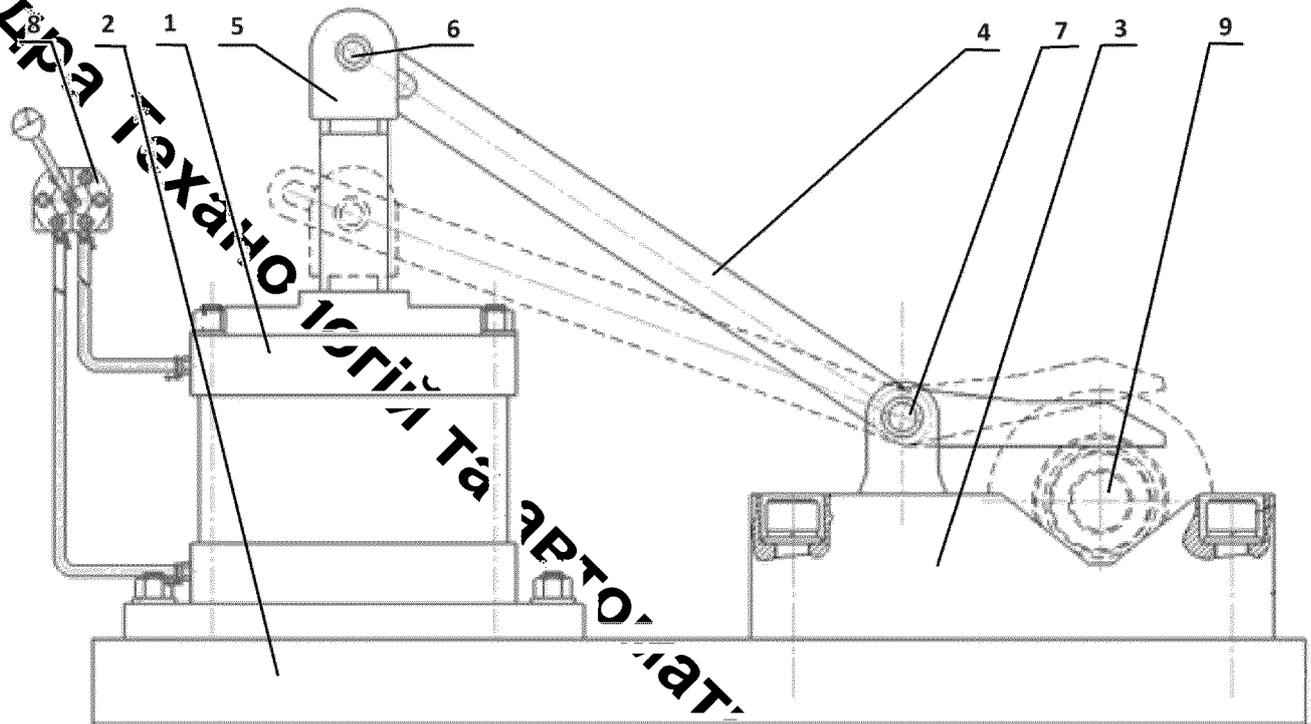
Ескіз спеціального пристосування для шпоночно-фрезерної операції 020
